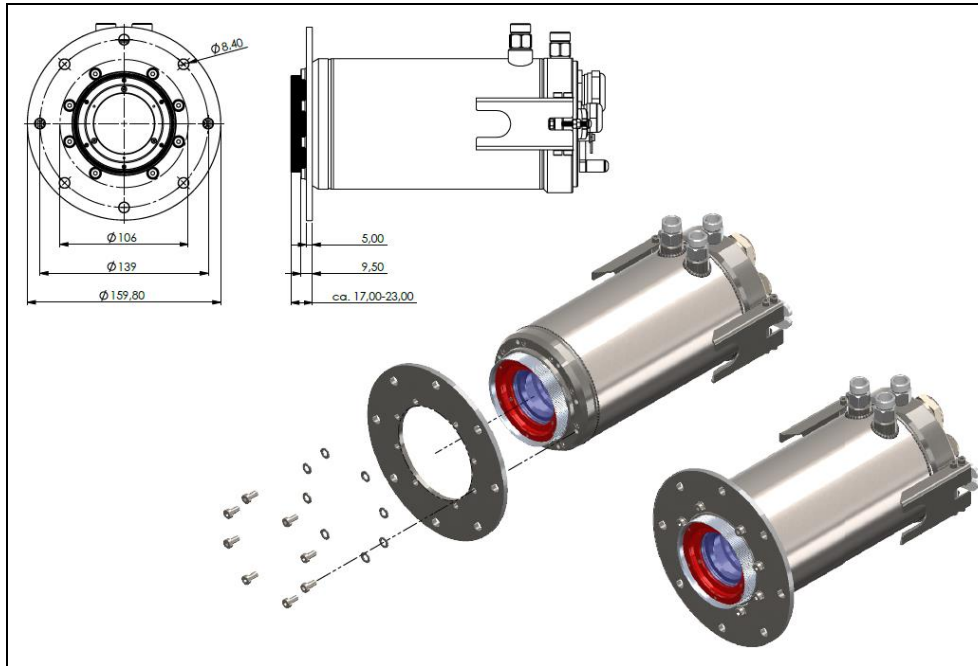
Montageflansch für Cooling Jacket Advanced (Standard und Extended)
